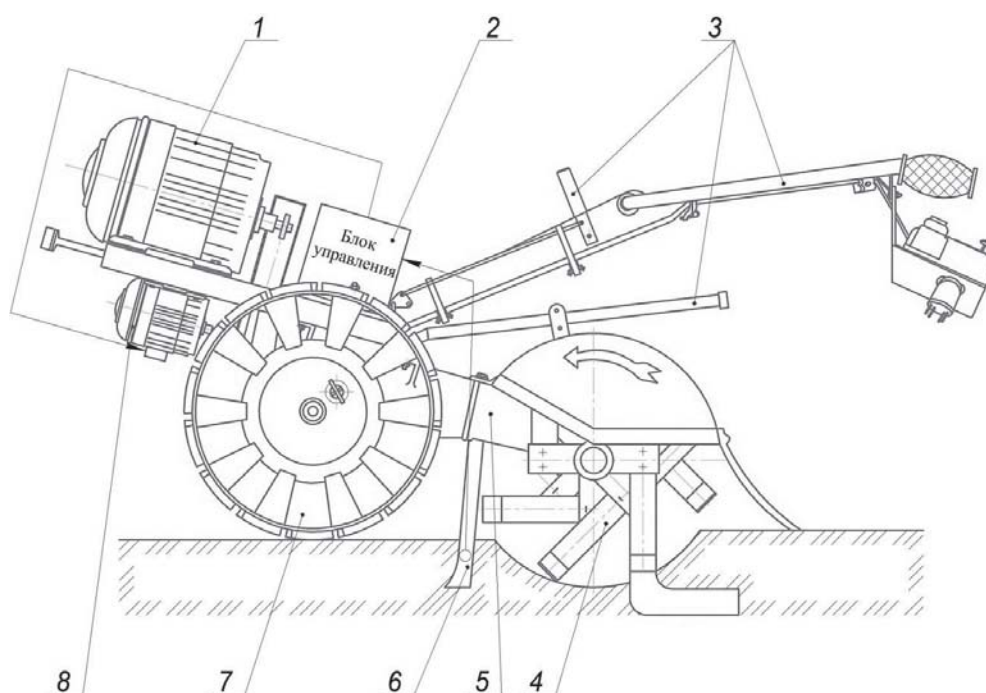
Схема СМПФА. На схеме обозначены: 1 – электродвигатель привода рабочих органов; 2 – блок управления с обратной связью; 3 – органы управления; 4 – рабочие органы; 5 – редуктор; 6 – сканер твердости почвы; 7 – ходовые колеса; 8 – электродвигатель привода ходовых колес.
